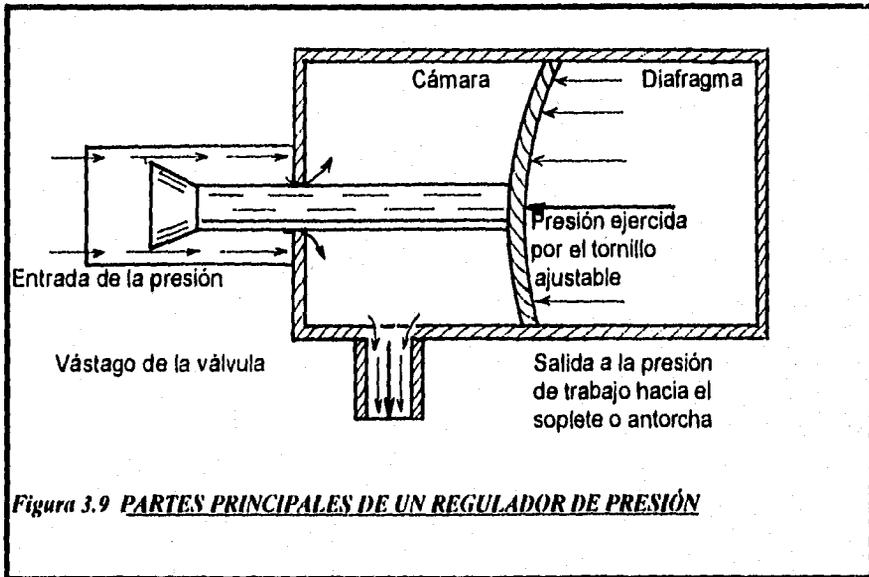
PARTES PRINCIPALES DE UN REGULADOR DE PRESIÓN
